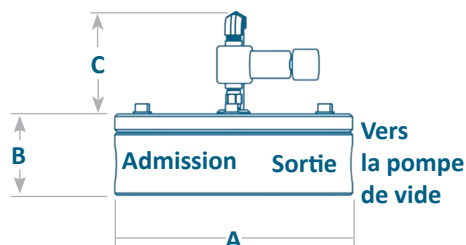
Schéma dimensionnel pour les régulateurs à ligne de 1/4" à 1"
